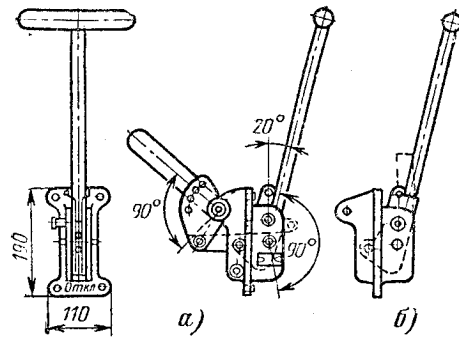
Привод ручной рычажный типа ПР-3.
